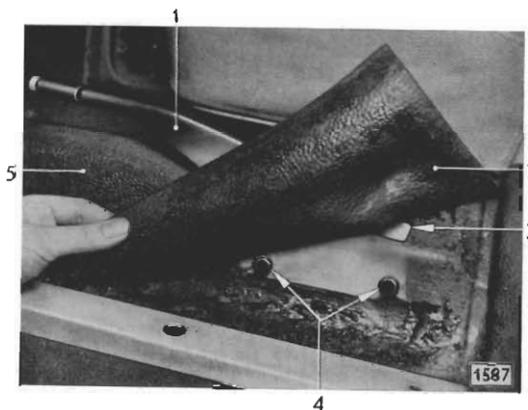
Zusammenbau Handbremshebel am Gelenkwellentunnel befestigt
